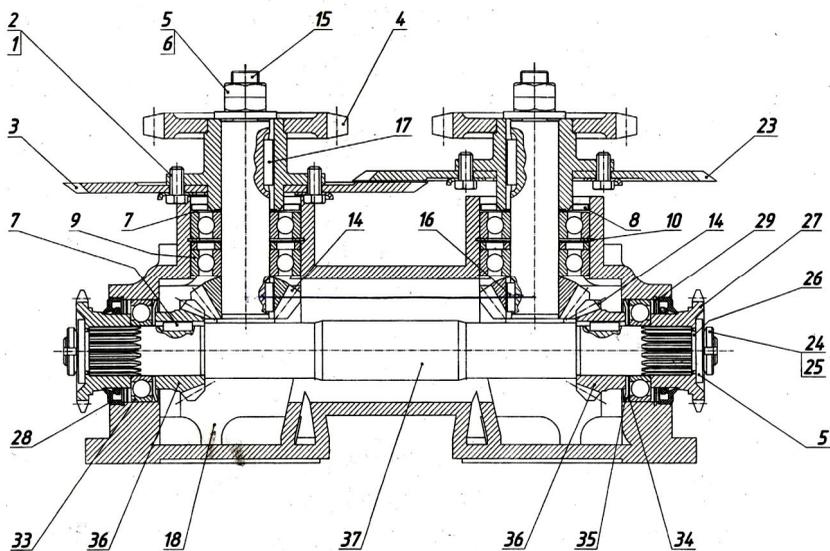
Приводная Коробка ПЗС 02.000: 1 – планка; 2- болт; 3 – нож; 4 – звездочка; 5 – шайба; 6 – гайка; 7 – шайба регулировочная; 8 – шайба защитная; 9 – подшипник 180307 ГОСТ 8882-75; 10 – кольцо пружинное внутреннее; 11 – шайба регулировочная; 12 – втулка; 13 – втулка; 14 – колесо зубчатое; 15 – вал; 16 – шпонка; 17 – шпонка; 18 – корпус; 19 – прокладка; 20 – пробка; 21 – шайба регулировочная; 22 – шайба регулировочная; 23 – звездочка; 24 – гайка; 25 – шайба; 26 – кольцо; 27 – полумуфта; 28 – манжета; 29 – кольцо внутреннее пружинное; 30 – шайба регулировочная; 31 – шайба регулировочная; 32 – шайба регулировочная; 33 – подшипник 207ГОСТ 8338-75; 34 – шайба регулировочная; 35 – маслоотражатель; 36 – колесо зубчатое; 37 – вал.
